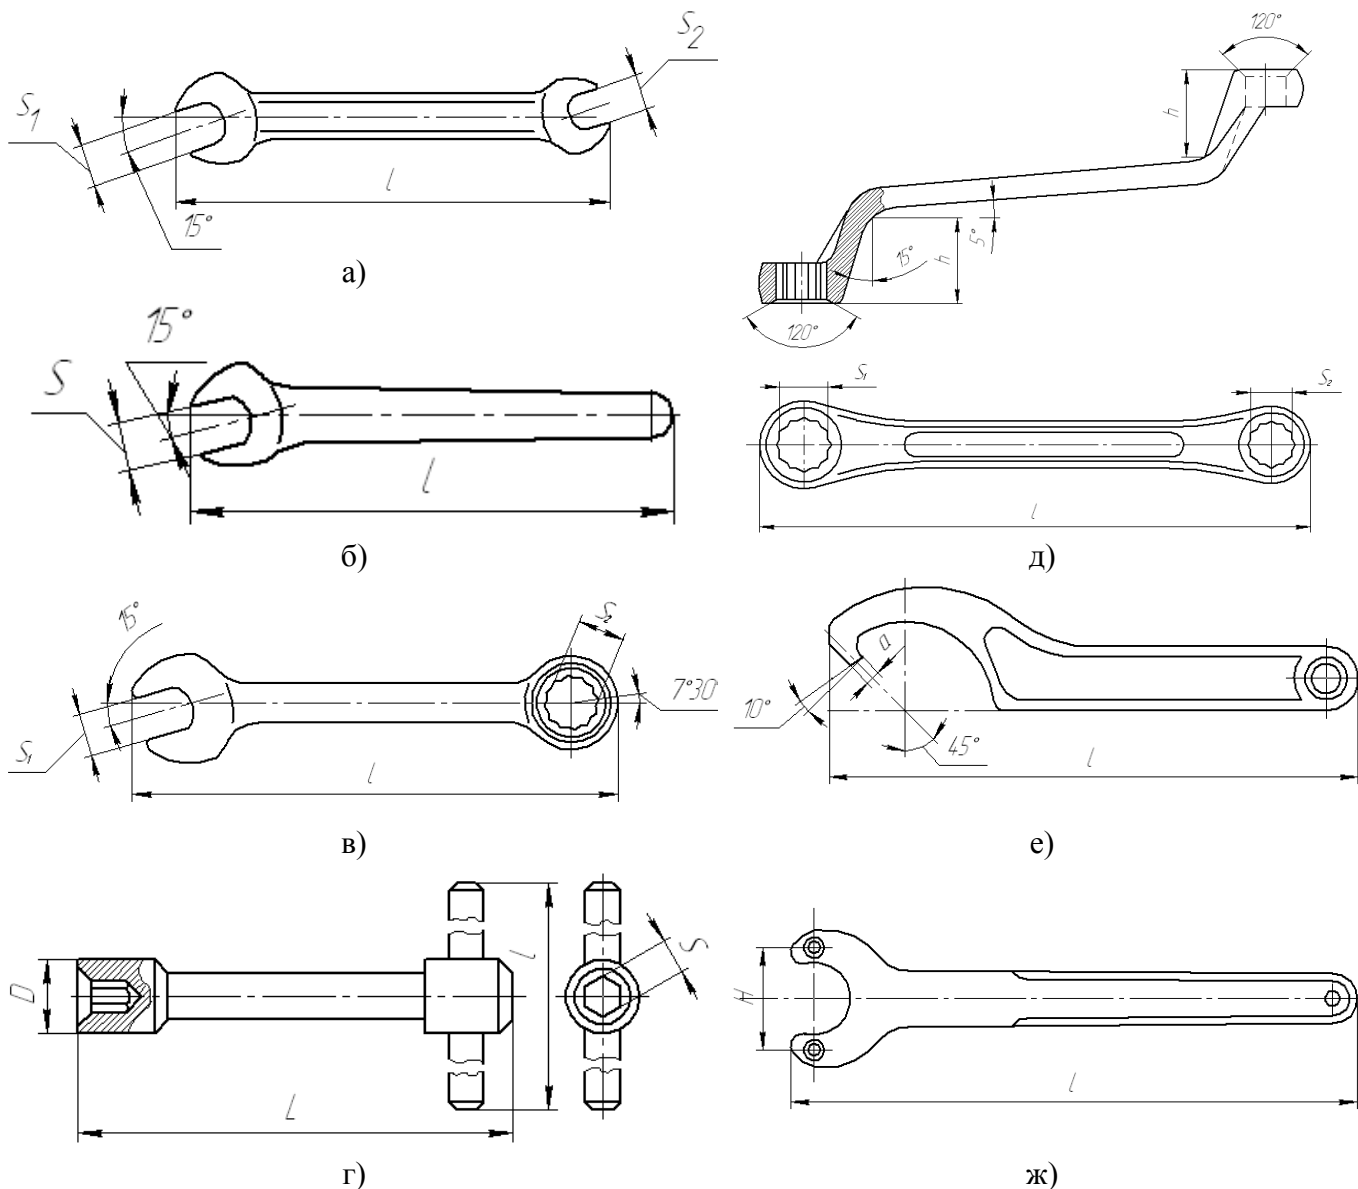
Инструмент ручной для разборки резьбовых соединений:
